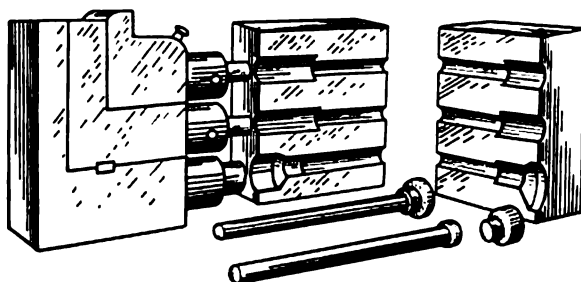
Jeu de poinçons et de matrices d'une machine à forger horizontale
